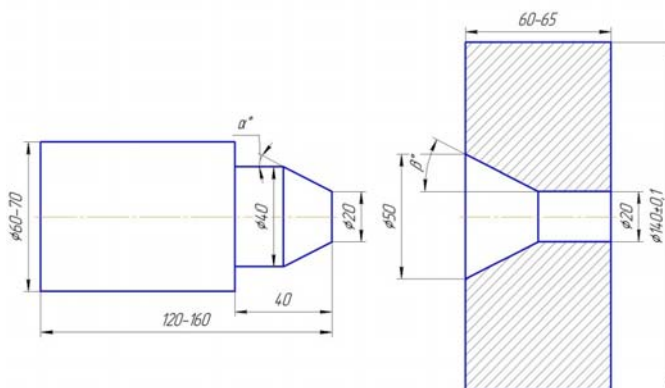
Эскиз имитатора штуцера и корпуса модели штуцерного узла
